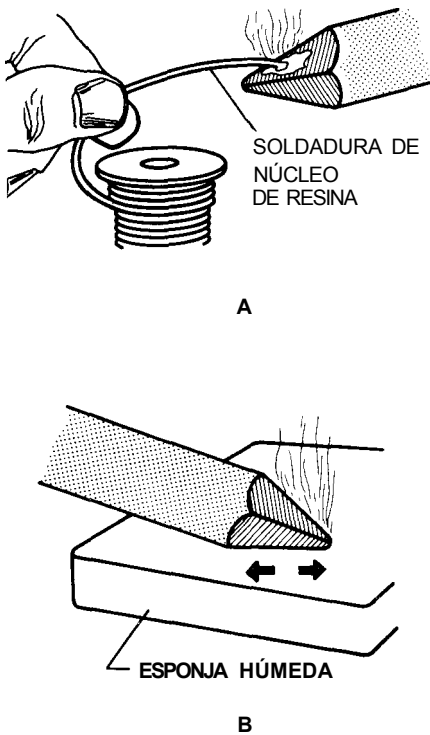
Preparación de la punta del caudín para su empleo: (A) estañado; (B) eliminación del exceso de soldadura.
